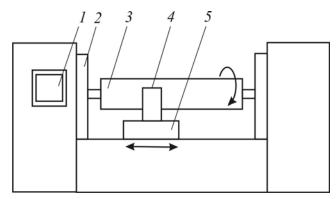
Электронно-механический гравировальный автомат для изготовления форм глубокой печати: I — пульт управления; 2 — телескопический кожух; 3 — формный цилиндр; 4 — режущая головка; 5 — каретка
